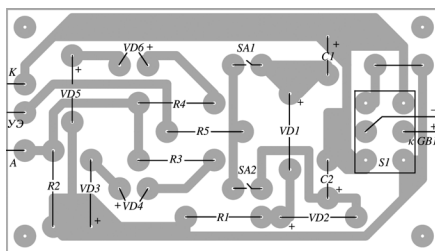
Эскиз монтажной платы испытателя. Вид со стороны установки деталей.
